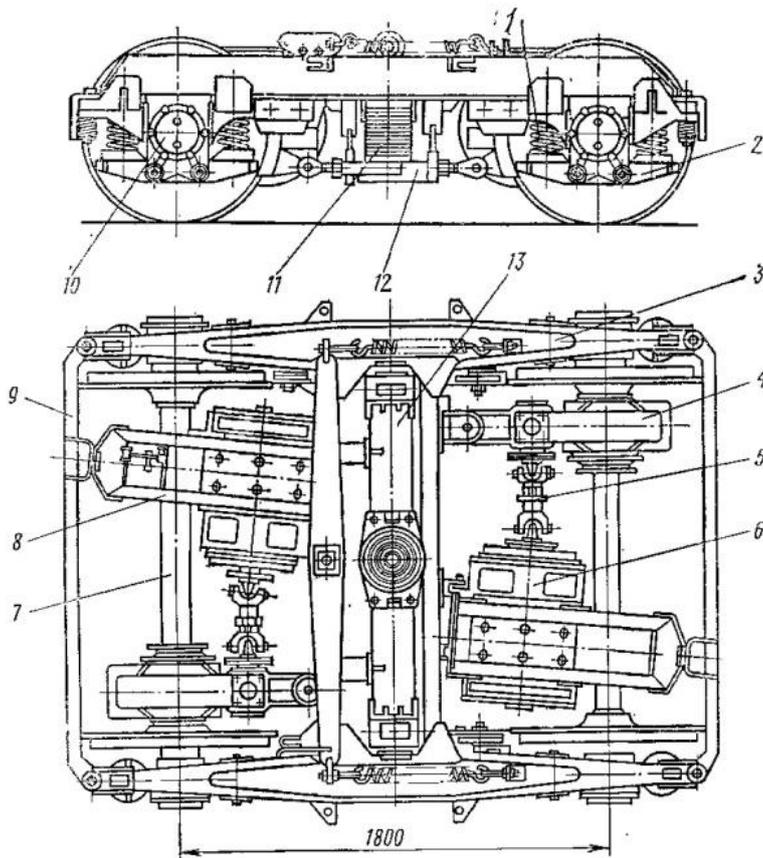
Схема вагонной тележки трамвая. 1 – цилиндрические пружины; 2 – балансиры; 3 – рама; 4 – редуктор; 5 – карданный вал; 6 – тяговый двигатель; 7 – ось колесной пары; 8 – балка; 9 – поперечная траверса; 10 – корпус буксы; 11 – листовые рессоры; 12 – балка-люлька; 13 – шкворневая балка.
